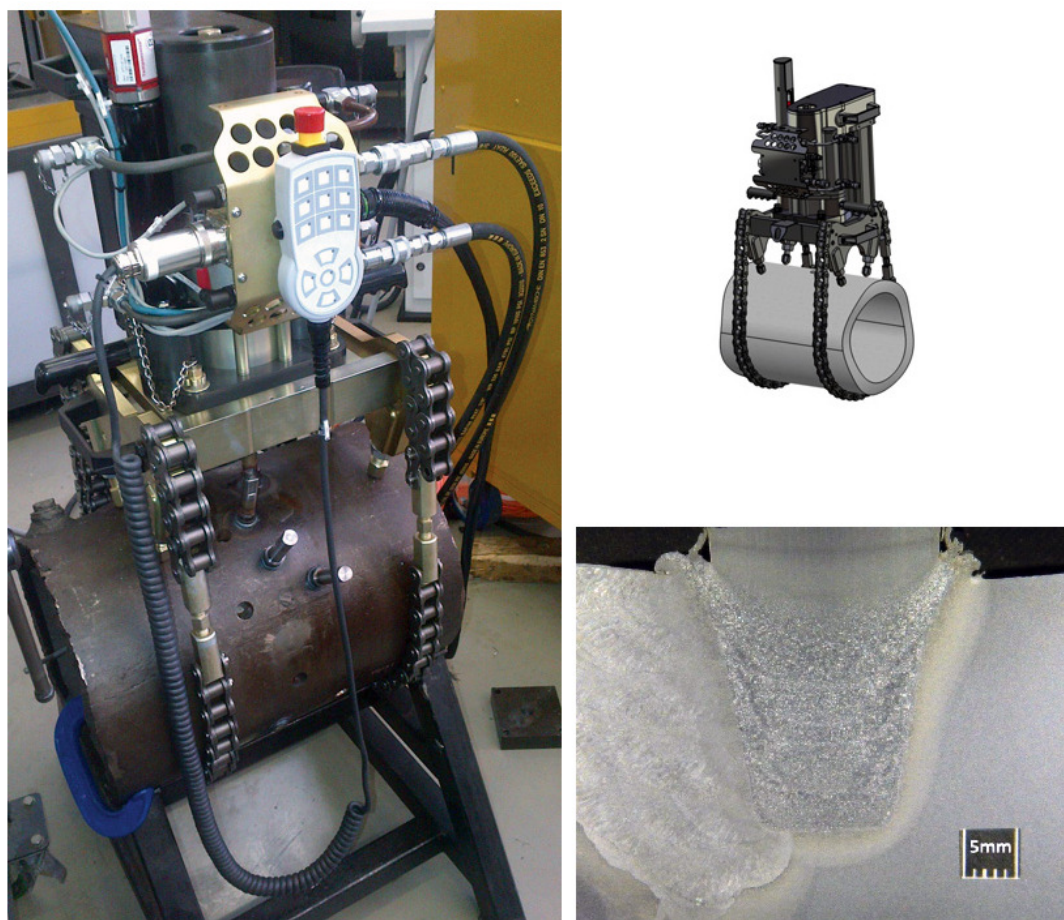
Máquina Portátil de Solda por Atrito Contínua (PCFWM) ([www.mantacor.co.za](http://www.mantacor.co.za) – Acesso: 19/06/2016).
